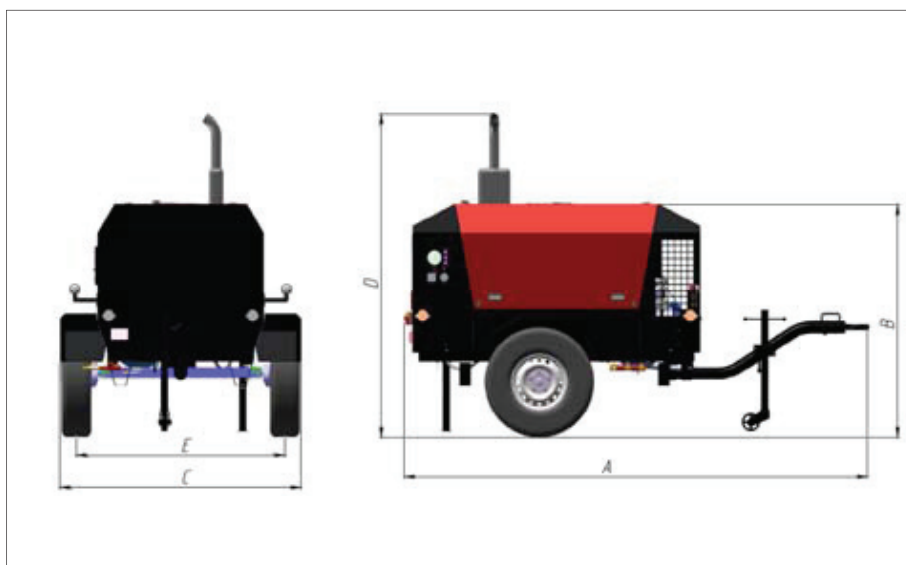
Габаритные размеры компрессорной станции «Вітер Д»
